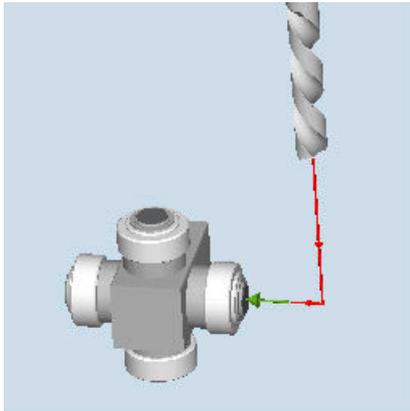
Messen Länge: Bohrer (CYCLE982), Beispiel Werkzeuglage: ↓ radiale Stellung
